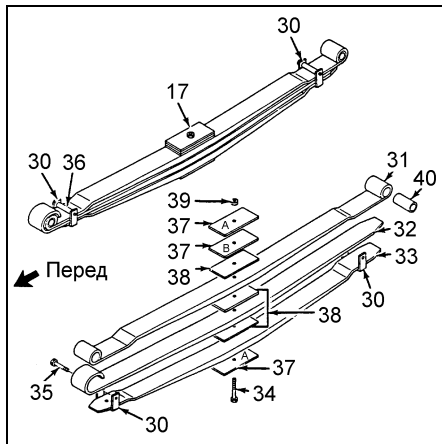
Разборка и сборка передней рессоры. 17 - рессора в сборе, 30 - хомут листов рессоры, 31 - лист №1, 32 - лист №2, 33 - лист №3, 34 - центральный болт рессоры, 35 - болт хомута, 36 - дистанционная втулка хомута, 37 - подкладка, 38 - прокладки, 39 - гайка центрального болта, 40 - втулка рессоры.
